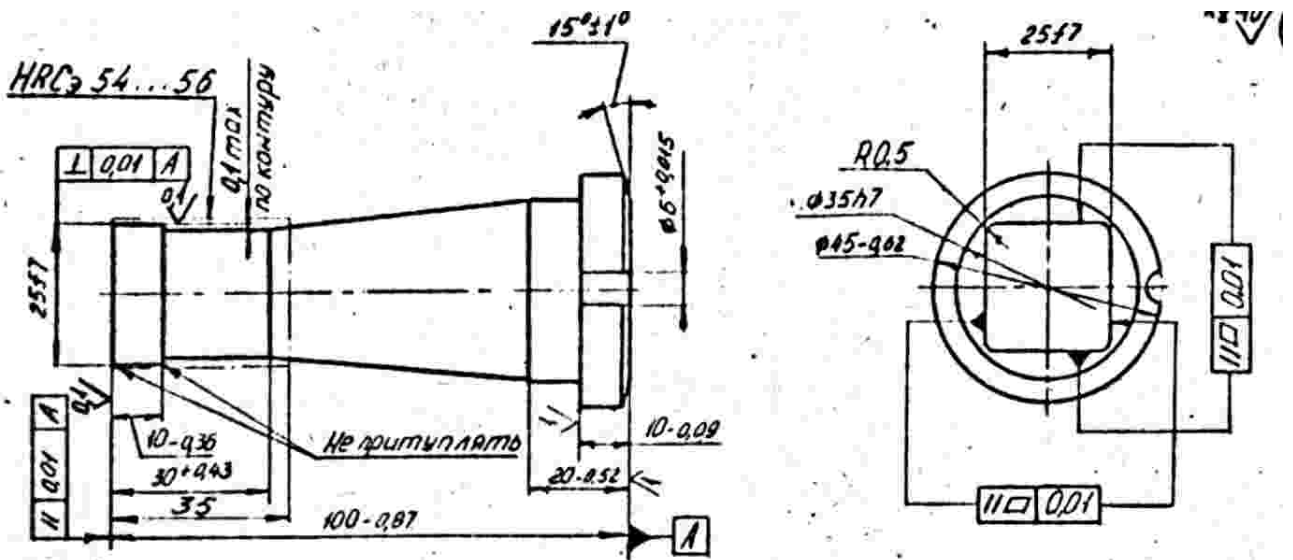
Конструкция пуансона прямоугольной формы без стержня
